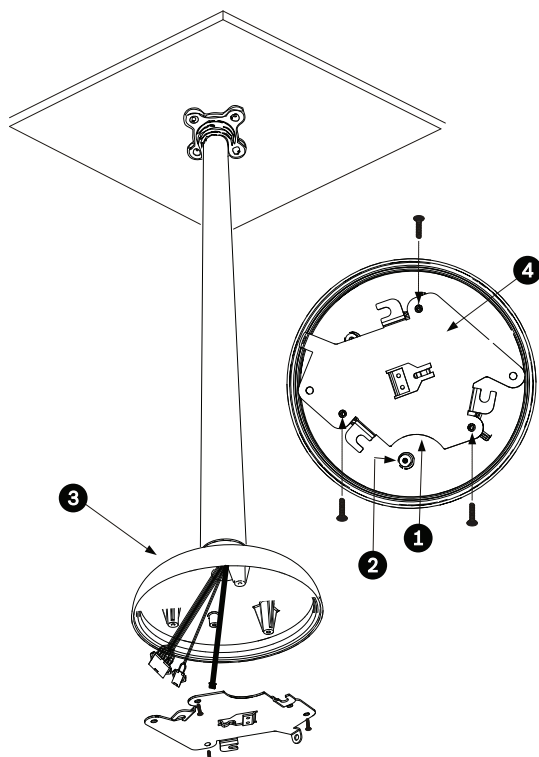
Fixar o suporte pendente para montagem em tubo ao tecto
